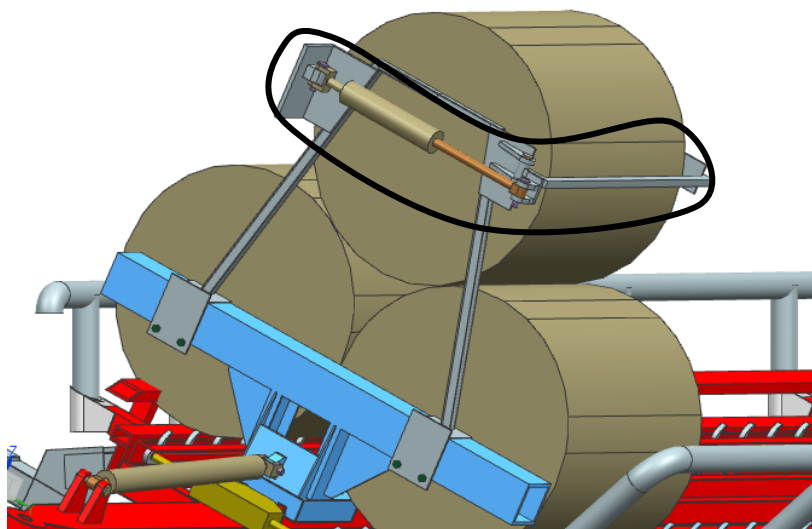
Základní pohled na 3D CAD model a popis částí – 1
